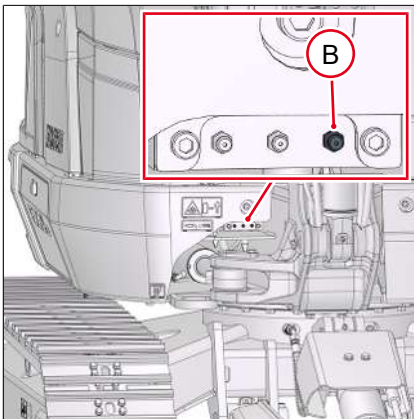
Punto de lubricación del engranaje de la corona de giro
